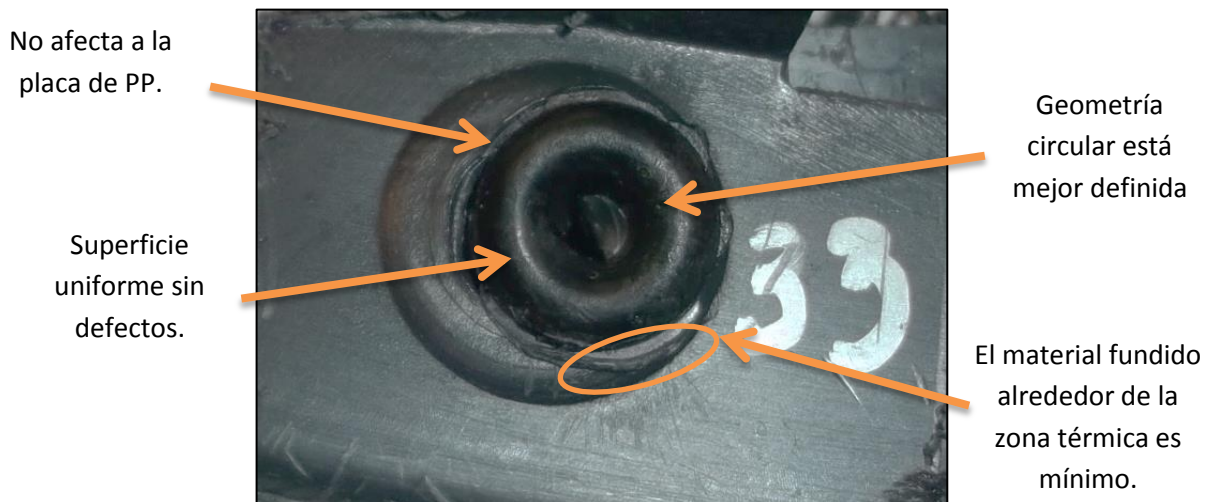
Soldadura circular con mayor fuerza de desprendimiento.
